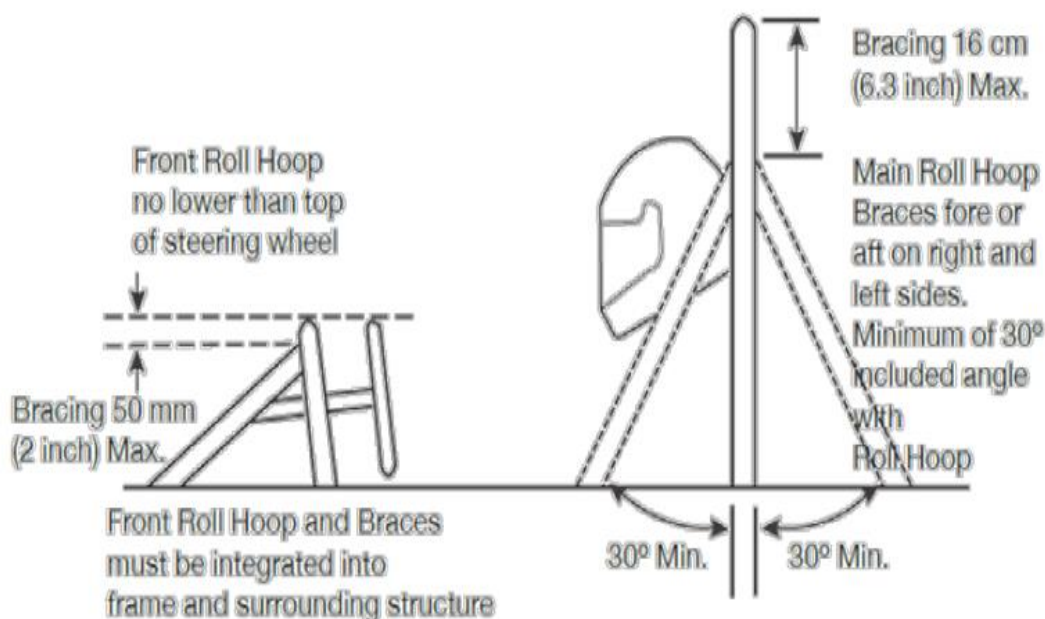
Схема крепления распорок к передней и главной дуге
